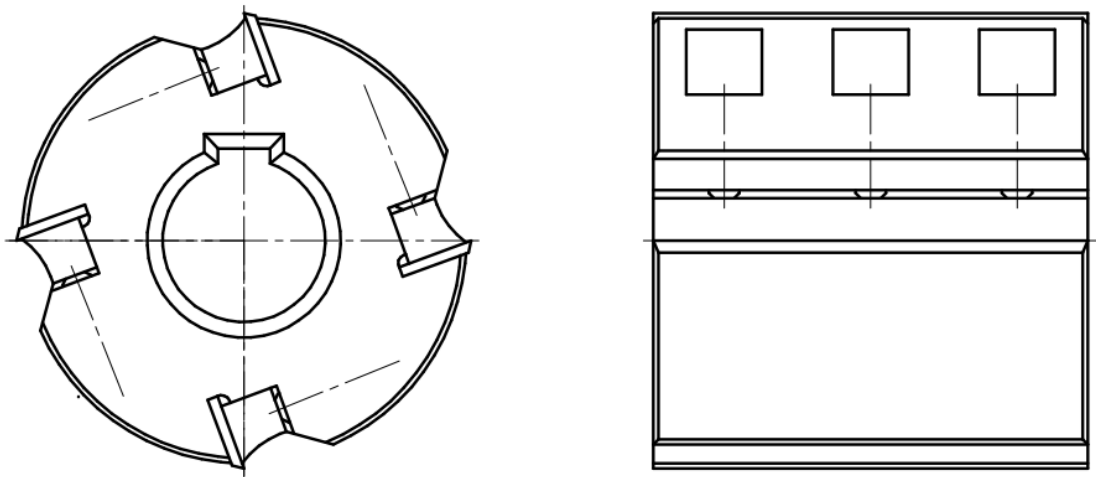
Циліндрична фреза зі змінними ножами
